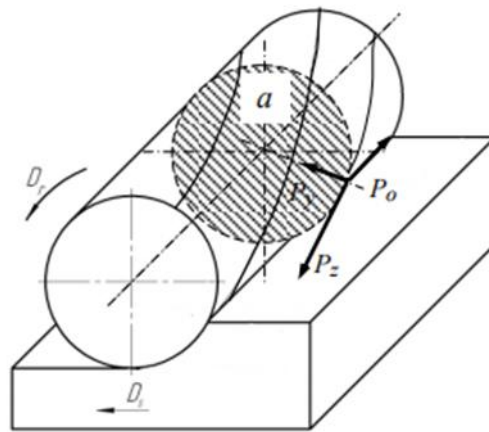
Силы резания на примере цилиндрического фрезерования фрезой с винтовым зубом.
